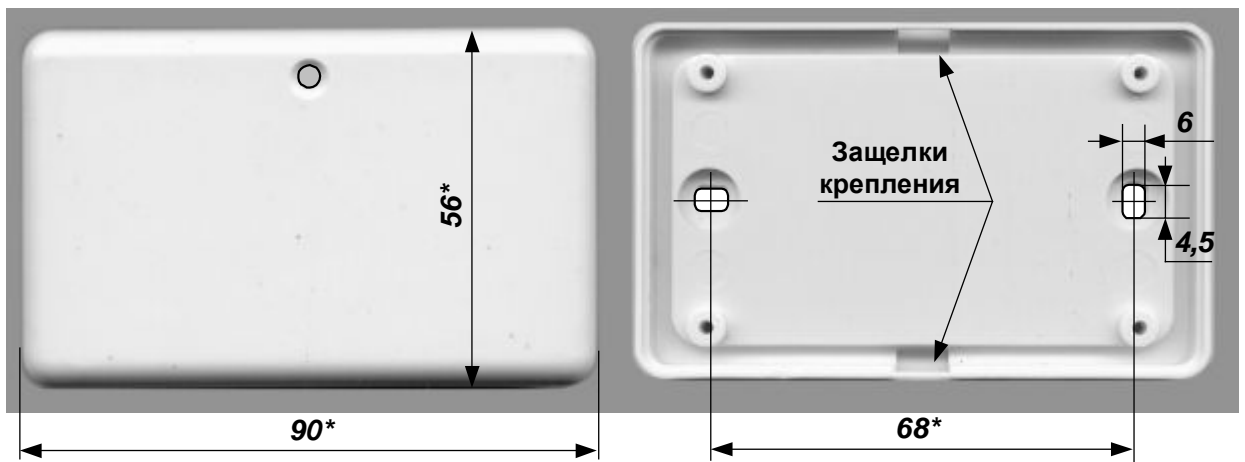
Габаритные и присоединительные размеры корпуса ИСМ-22 исп.08-1
